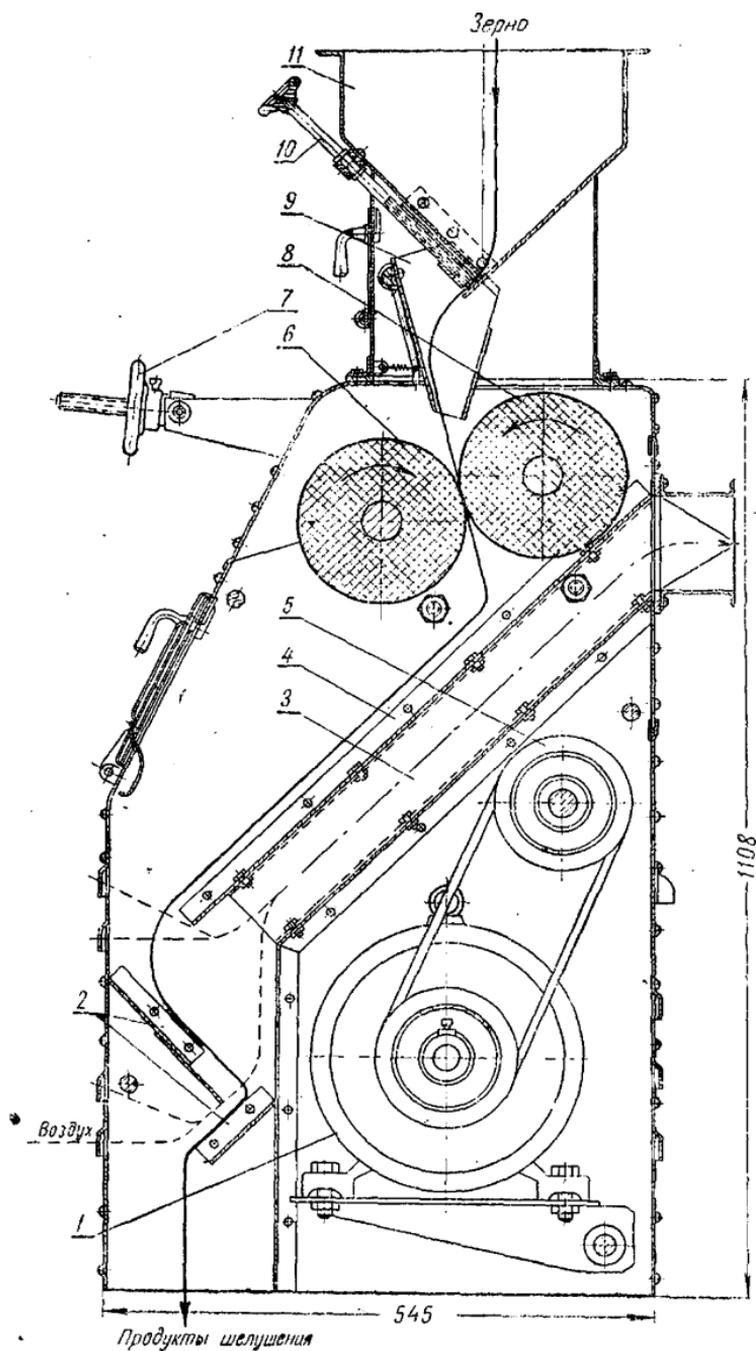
Шелушитель с резиновыми валками ЗРД-2,5.
